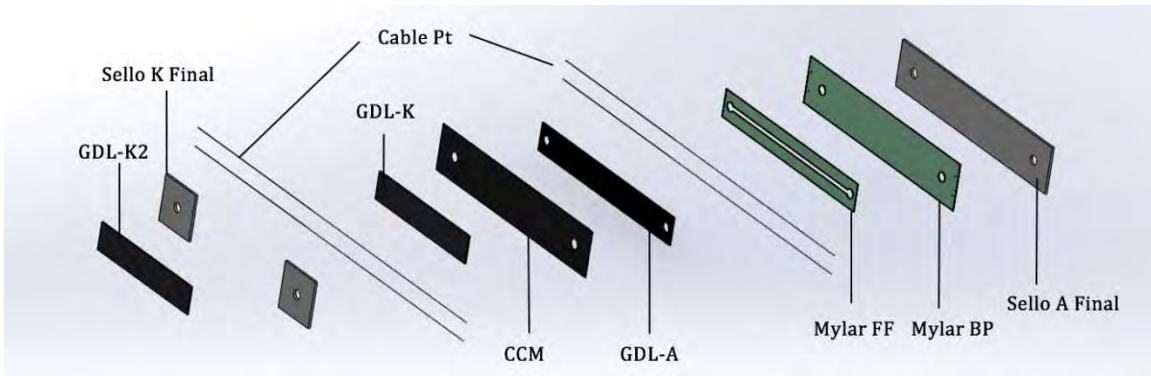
Celda 2 con vista explosionada en SolidWorks.
